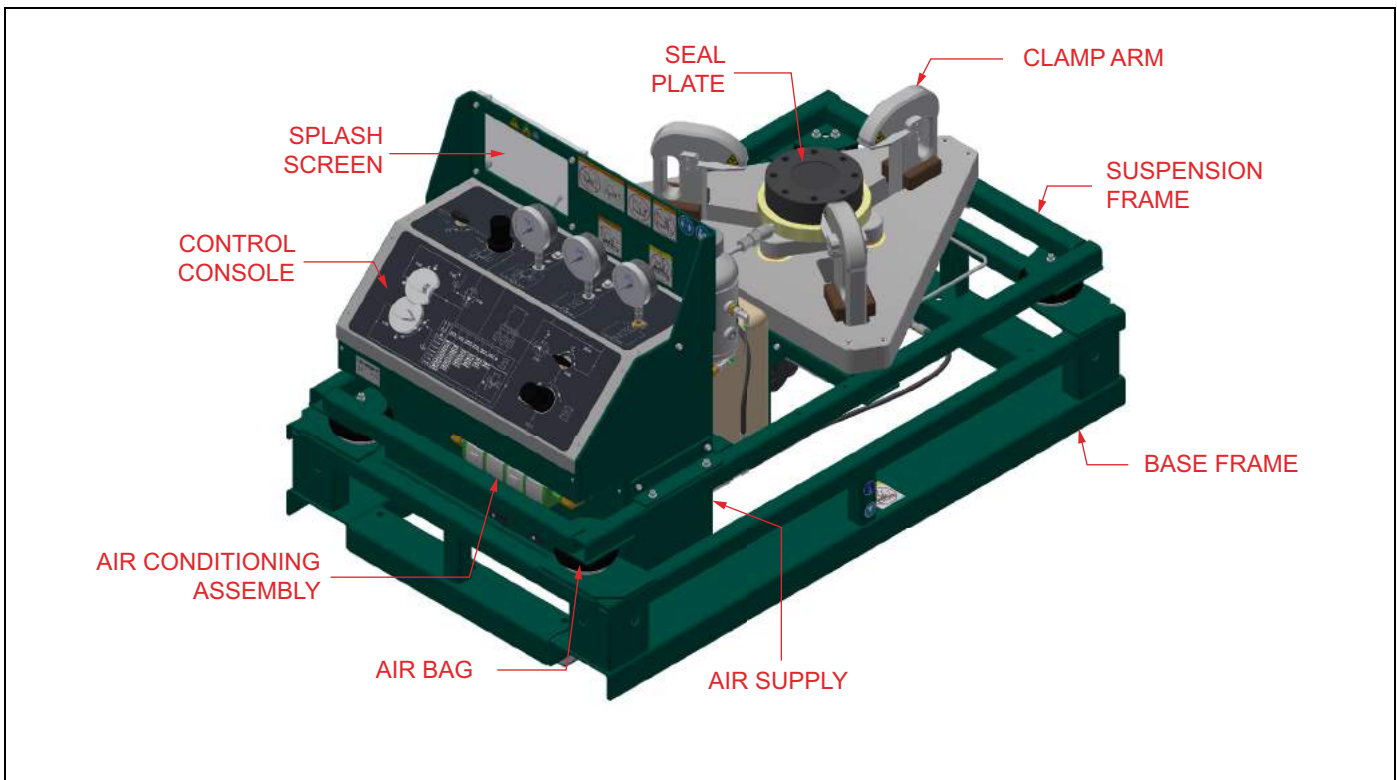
COMPONENTES DE LA PARTE FRONTAL
